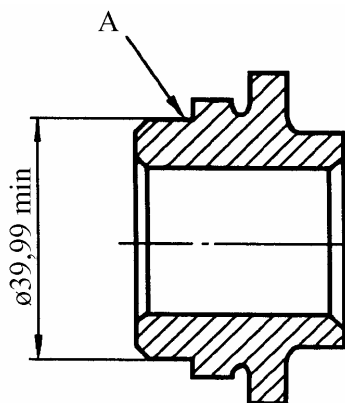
Муфта подшипника выключения сцепления – 2101-1601185:
